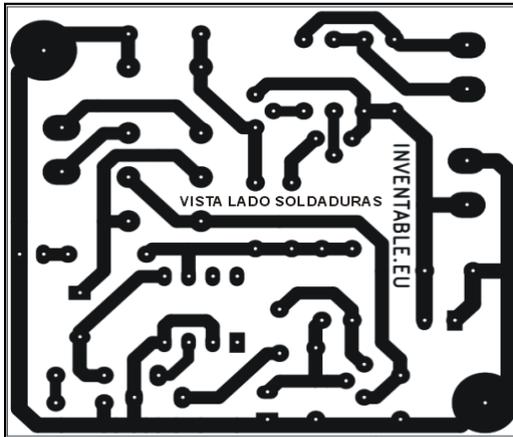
Vista lado soldaduras del circuito impreso.
